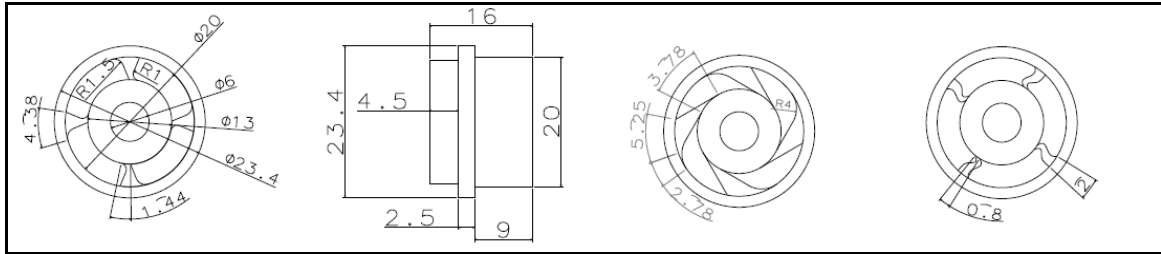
Deney yapılan vorteks tüpün 3 boyutlu çizimi
